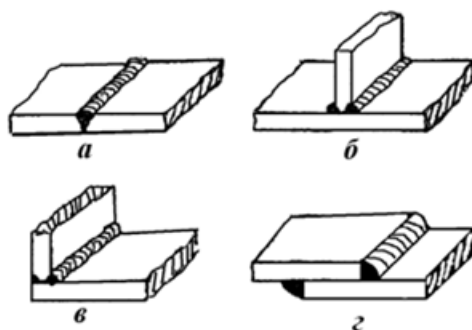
Типы сварных соединений: а - стыковое; б - тавровое; в - угловое; г – нахлесточное
